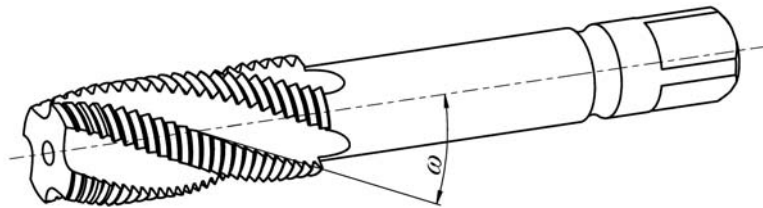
Общий вид метчика машинного с винтовыми стружечными канавками
